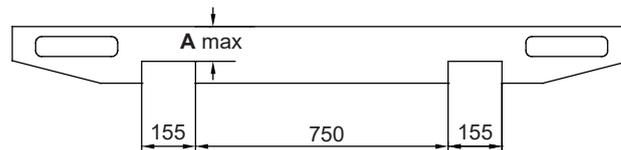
Z-45-110, Z-75-110, Z-45-90, Z-75-90
